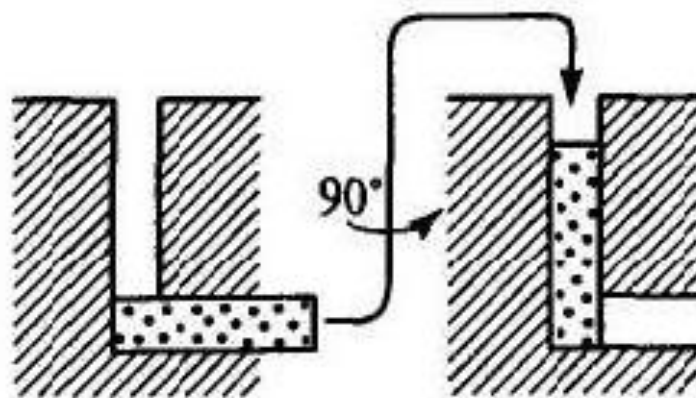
Поворот заготовки на угол  $90^\circ$
